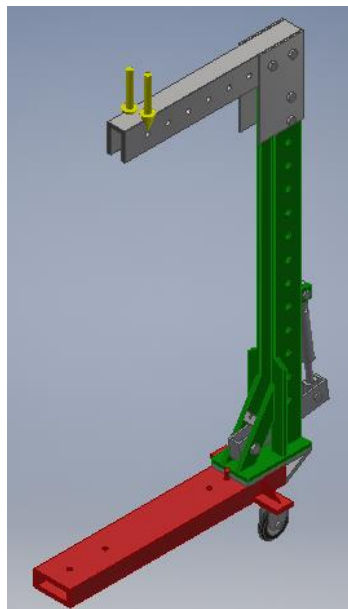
Vista de la máquina en conjunto sometida a cargas encima de la viga extensora Fuente:
